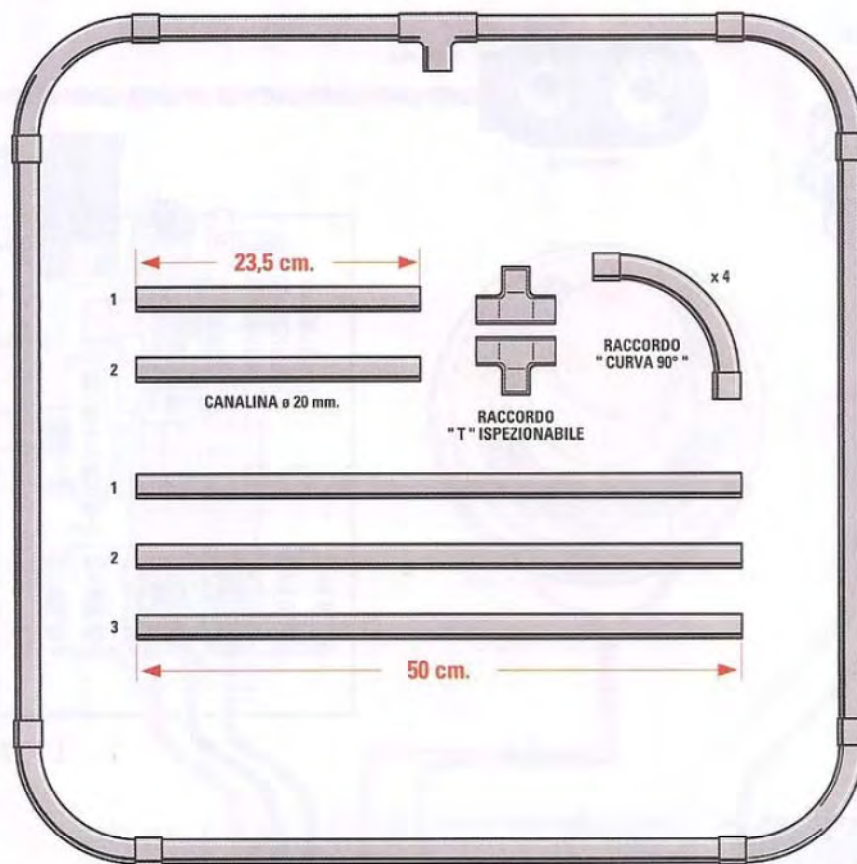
In questo disegno sono indicate le dimensioni delle componenti utilizzate per la realizzazione del nostro prototipo di bobina captatrice di forma quadrata.
